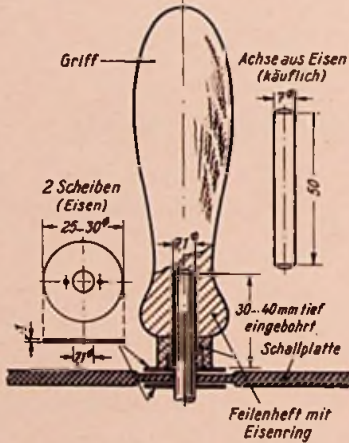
Die Pressvorrichtung im Schnitt. Gezeigt wird, wie der zu reparierende Mittelteil der Schallplatte mit dem Werkzeuggriff zwischen zwei Scheiben glattedrückt wird. Die 7-mm-Achse muß sich leicht im Griff drehen lassen
